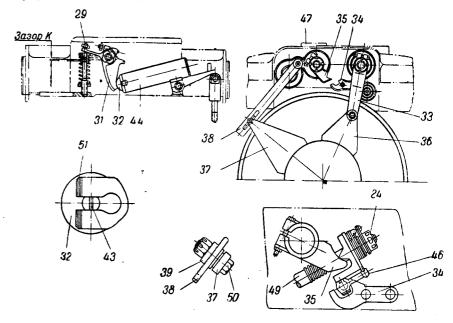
Привод к фрикционным элементам трехскоростного редуктора:
